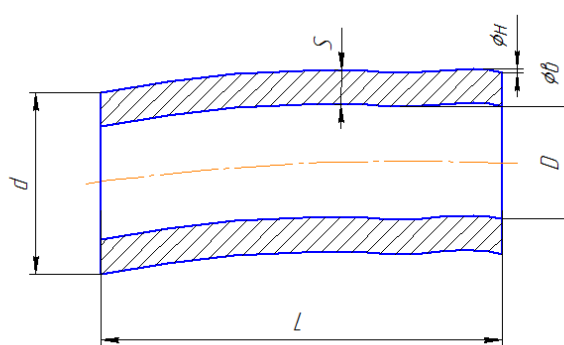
Схема нормируемых погрешностей стандартных трубных заготовок: D – диаметр ГО; d - наружный диаметр трубы; S – толщина трубы; ΔH - погрешность формы наружной поверхности трубы (волнистость); $\Delta в$ - погрешность внутренней поверхности трубы
